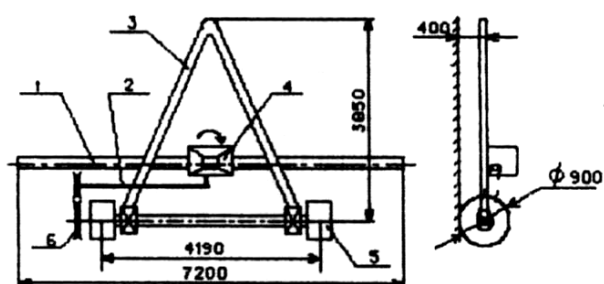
Общая схема расположения пружинно-транспортирующего рабочего органа для рассева сыпучих материалов по поверхности почвы на базе сцепки С-11:
